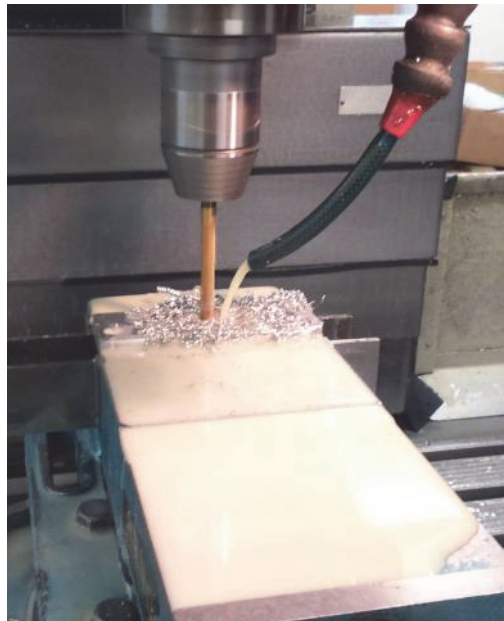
Bohren mit TiN-beschichtetem Werkzeug unter Vollschrnerung
